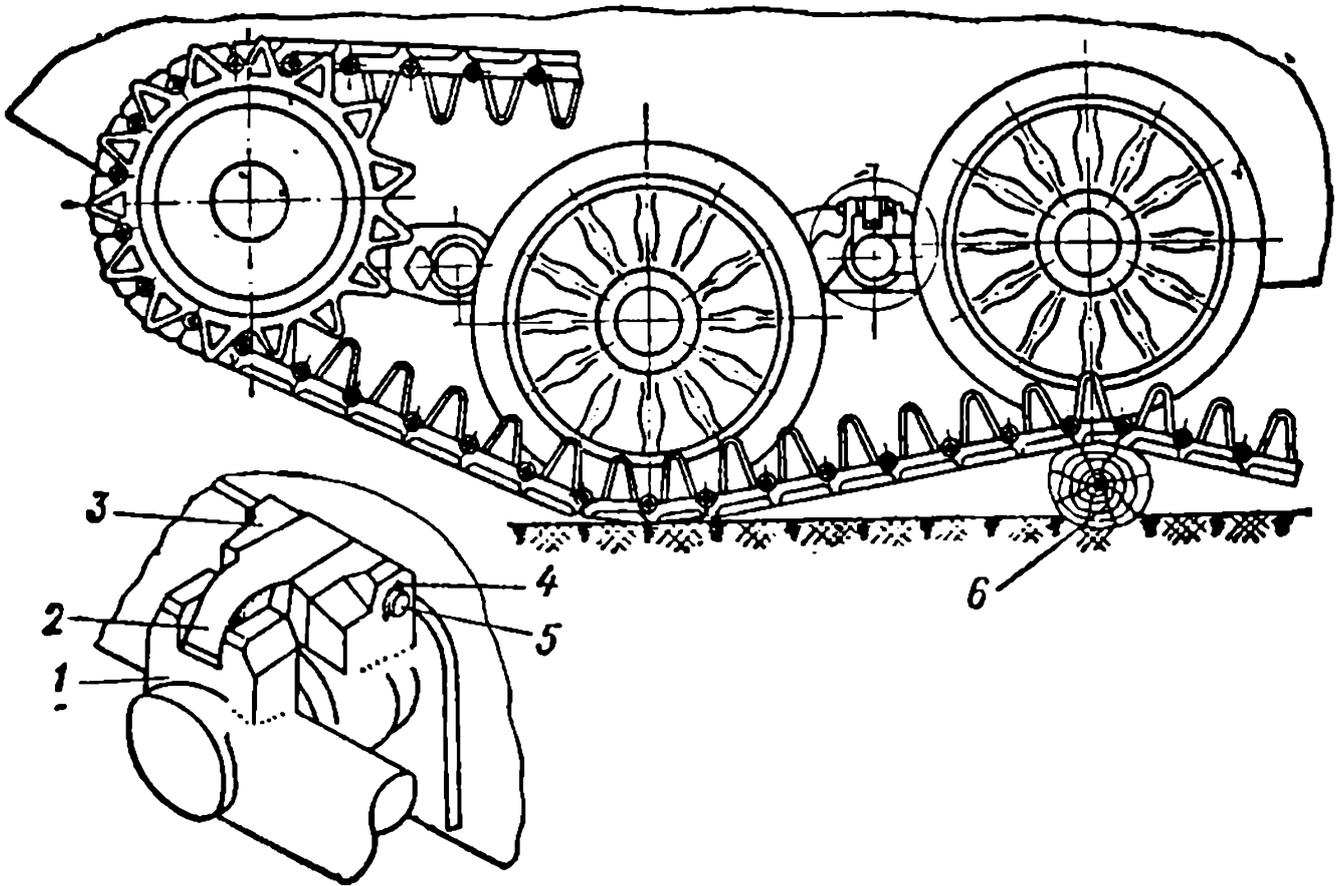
Приспособление для понижения клиренса и выключения подвески:
